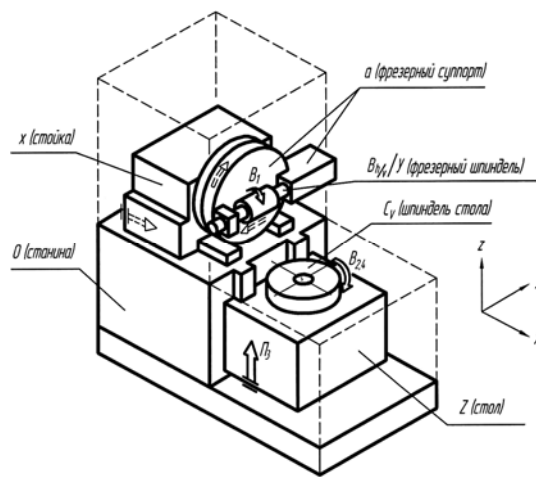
Компоновка зубофрезерного станка типа ВК3
